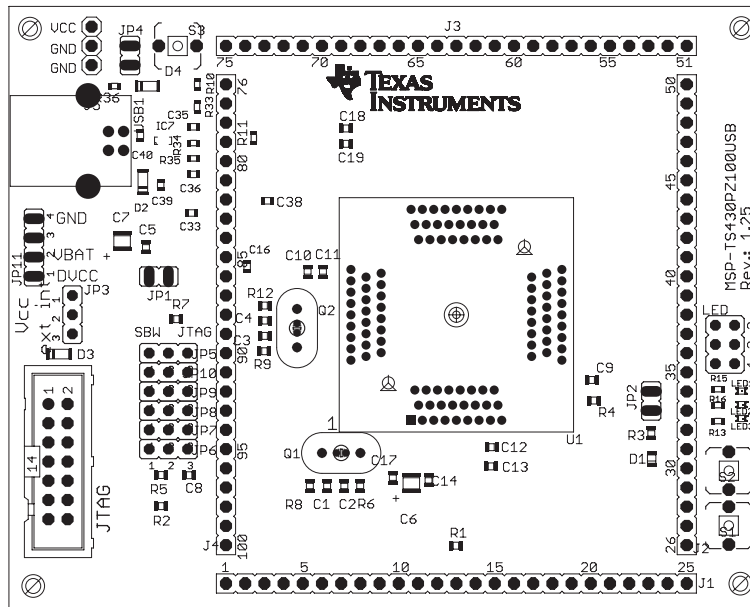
MSP-TS430PZ100USB 目标插座模块, PCB
